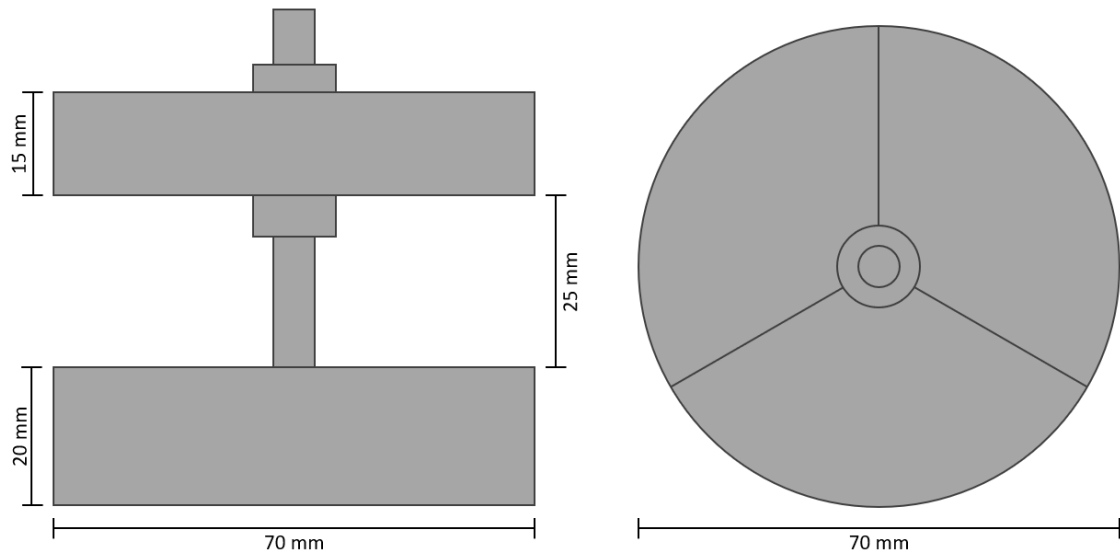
Detailskizze des Probenhalters; links: Frontansicht, rechts: Aufsicht
